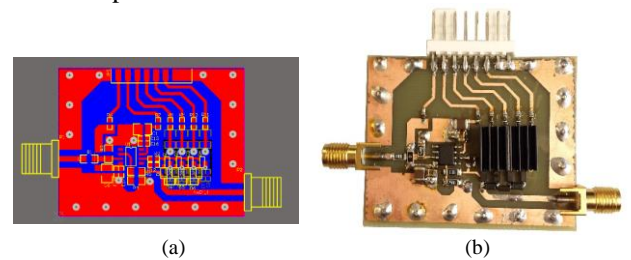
Diseño del PCB (a) y prototipo (b) del EA clase G implementado.
